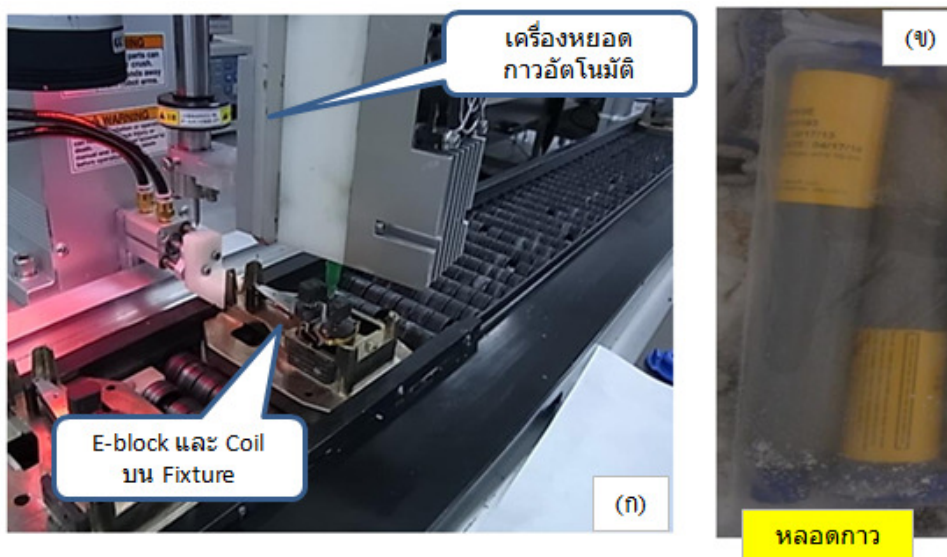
Coil bonding fixture, closing cover (ตัวล็อก Fixture) อลูมิเนียมขึ้นรูป (E-block) และขดลวดนำไฟฟ้า (Coil)
